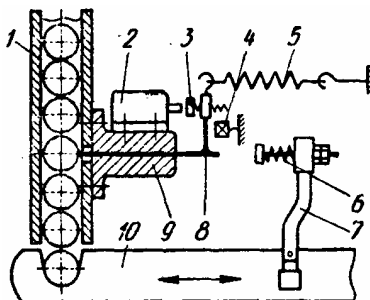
Механизм контроля наличия заготовок в лотке
